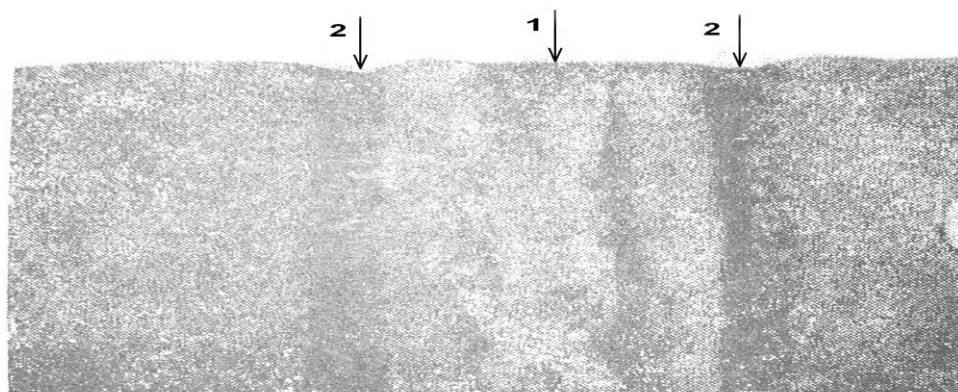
Коррозионное разрушение стальной конструкции в области сварного шва: 1 – сварной шов; 2 – коррозионное разрушение в околошовной зоне
